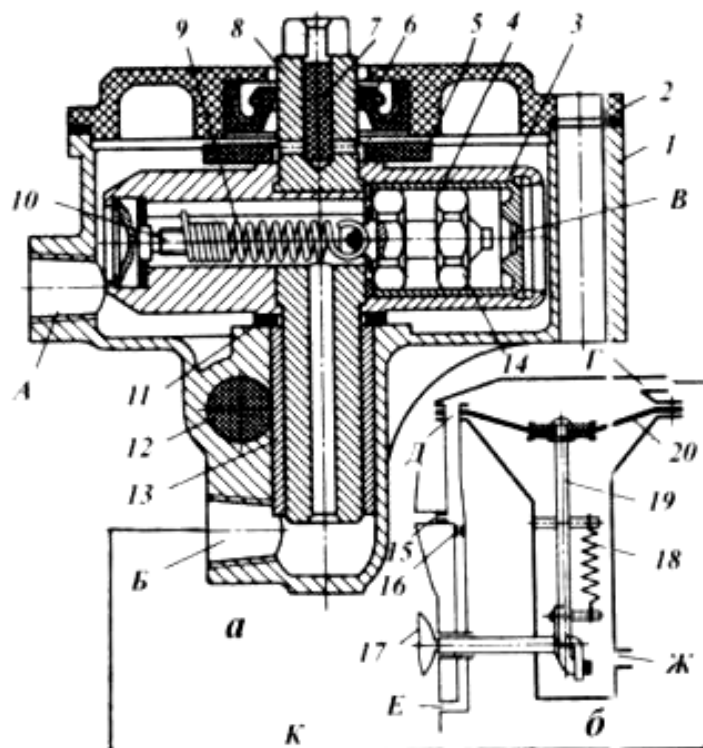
Ограничитель максимальной частоты вращения коленчатого вала: а – чувствительный элемент; б – исполнительный механизм; 1 – корпус датчика; 2 – крышка датчика; 3 – корпус ротора; 4 – седло клапана; 5 – опорная шайба; 6 – сальник; 7 – фитиль вала ротора; 8 – вал ротора; 9 и 18 – пружины; 10 – регулировочный винт; 11 – шайба ротора; 12 – фитиль втулки; 13 – втулка; 14 – груз датчика; 15 и 16 – воздушные жиклеры; 17 – дроссельная заслонка; 19 – шток диафрагмы; 20 – диафрагма; А и Ж – каналы подвода воздуха из воздушной камеры карбюратора; Б и Г – каналы датчиков; В – отверстие; Д и Е – каналы, сообщающие полость под диафрагмой с пространством соответственно перед дроссельной заслонкой и после нее; К – канал подвода воздуха от датчика к вакуумному исполнительному механизму
